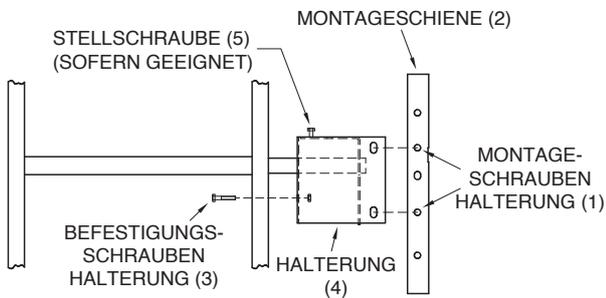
Detailzeichnung Leiter, Halterung und Montageschiene
